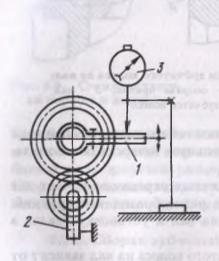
Схема контроля бокового зазора в зубчатом соединении
